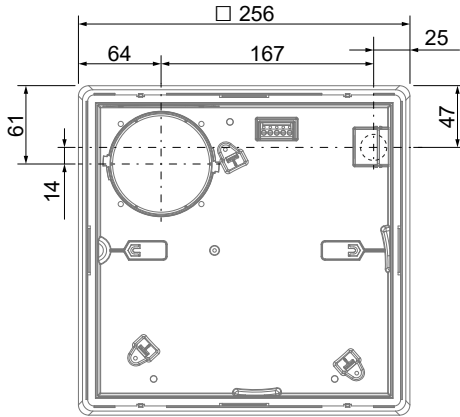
Maßzeichnung – Kabeldurchführung Gehäuse Abluftventilator Taris AP
